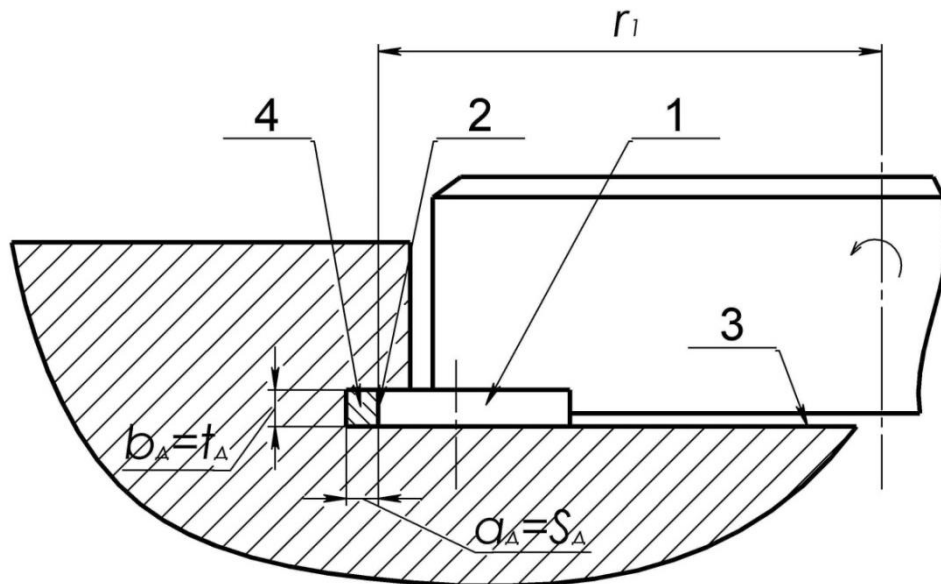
Схема різання додатковими різальними кромками фрези
